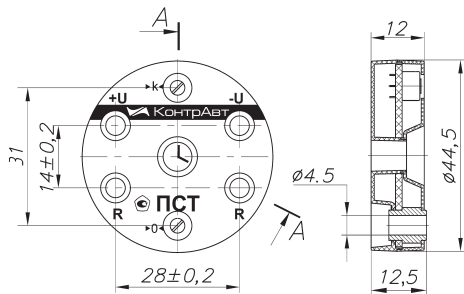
Внешний вид и габаритные размеры преобразователя ПСТ.
